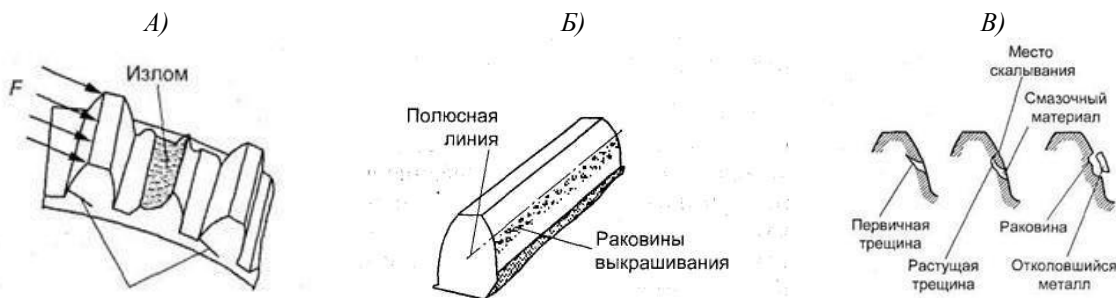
Типы усталостного разрушения зубьев зубчатого колеса: А) излом зуба; Б) выкрашивание; В) усталостные раковины.
